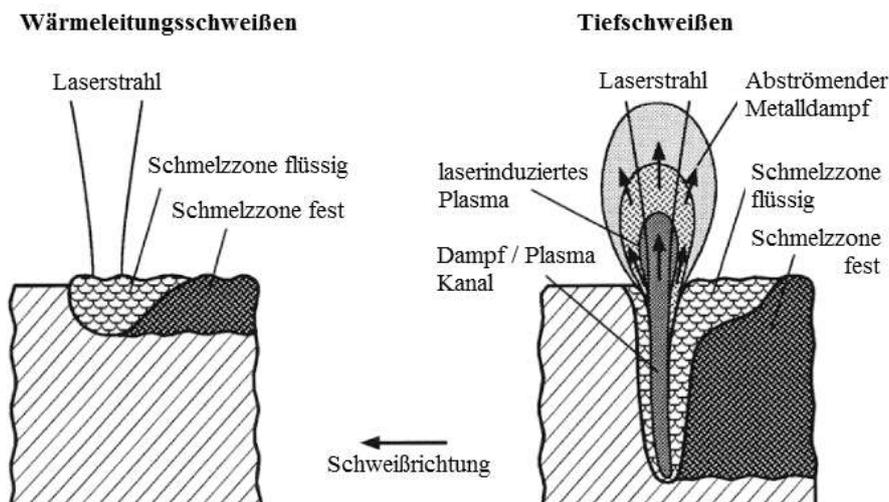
Prinzipien des Laserstrahlschweißens (Quelle: /2,S.5/)
